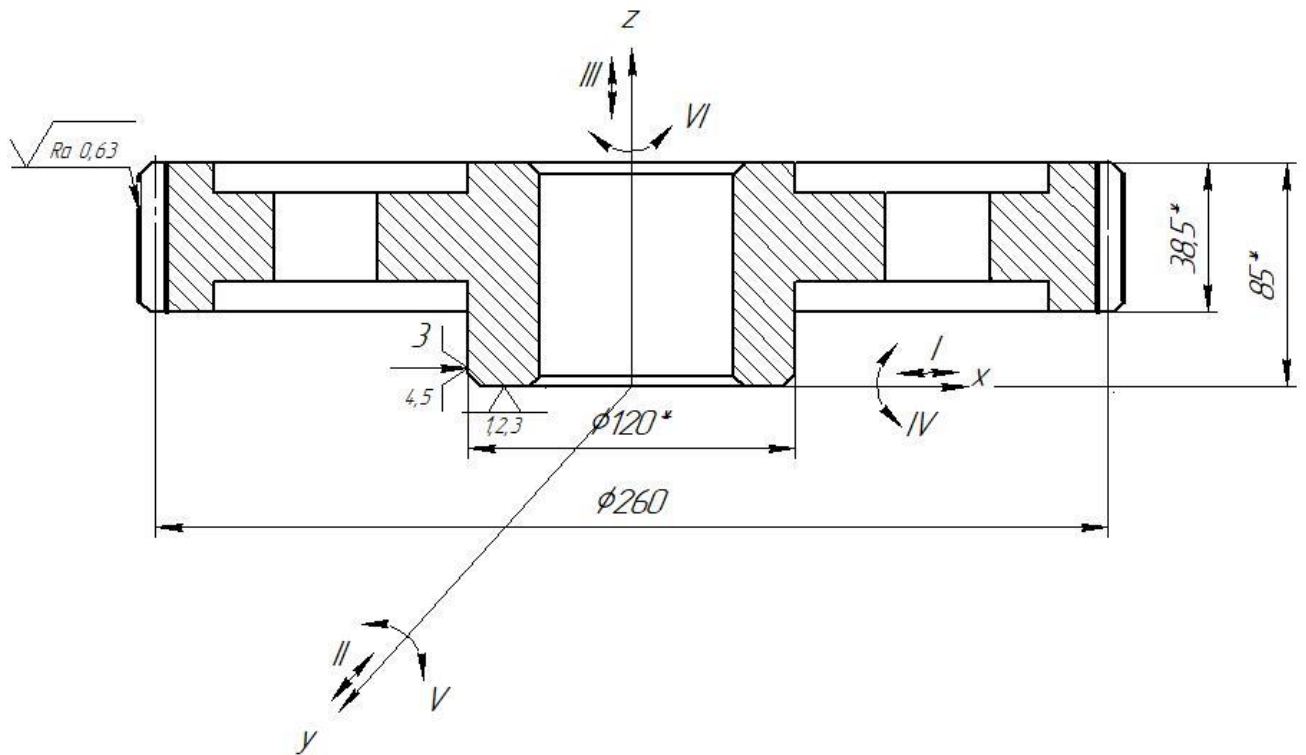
Базування деталі в трьох кулачковому патроні
